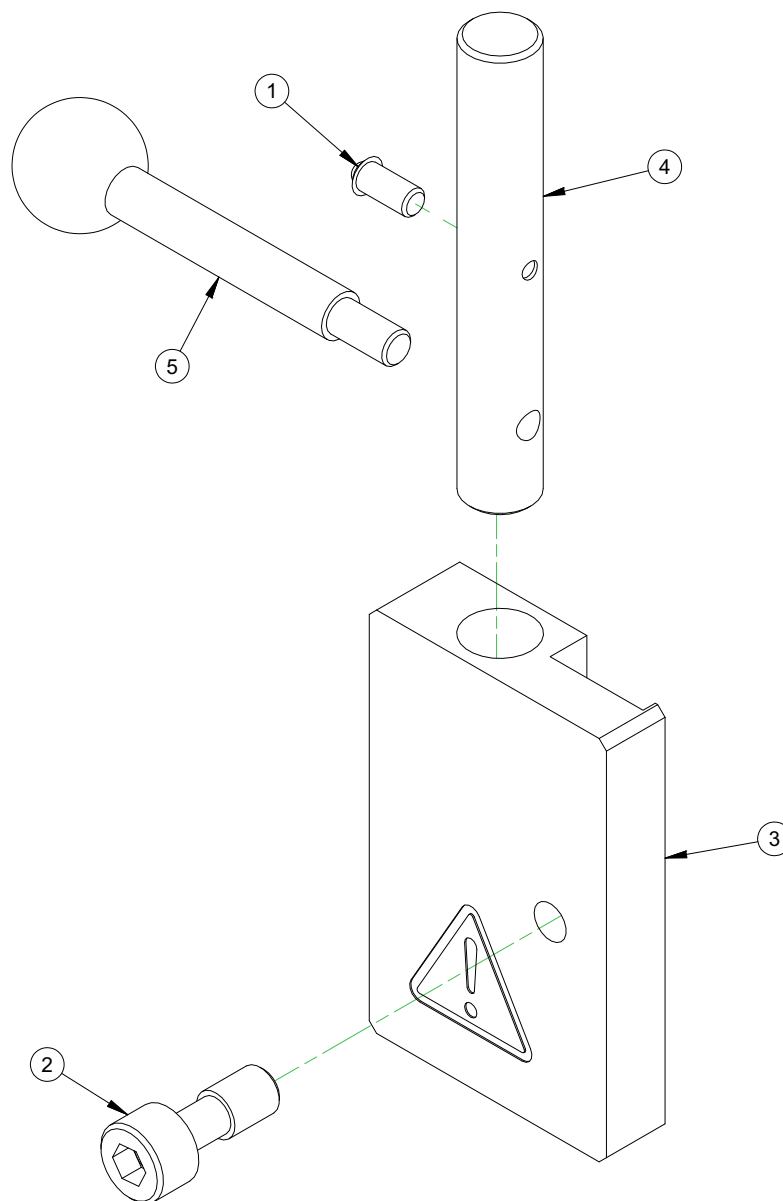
CONJUNTO DE LA CAJA DE ALIMENTACIÓN DEL CABLE DE TRACCIÓN (N/P 86900)
